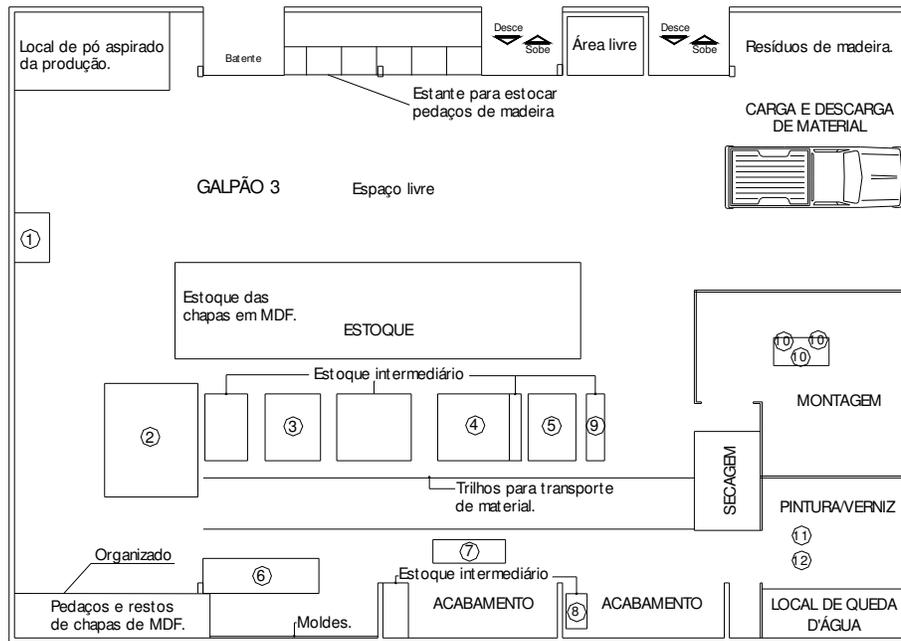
Planta baixa 6: Galpão 3 com lay-out modificado sem a linha de produtos sob encomenda. (Equipe de Projeto).
